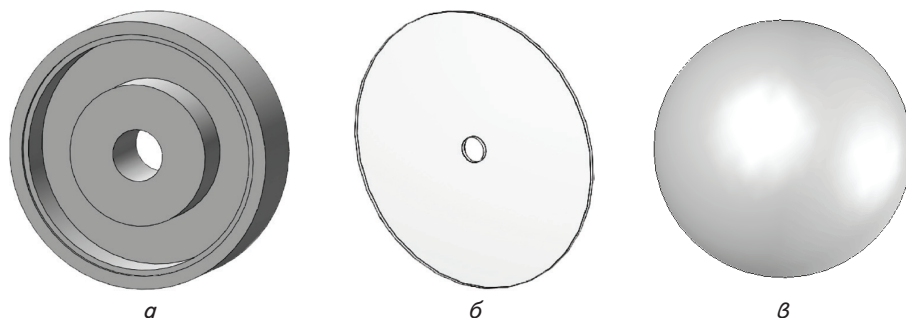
Детали 3D модели автобалансиров: а – корпус АБ; б – крышка; в – шар
